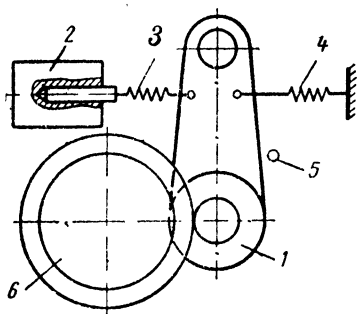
Способ прижима вала ведущего двигателя к обремененному шкиву ведущего вала.
